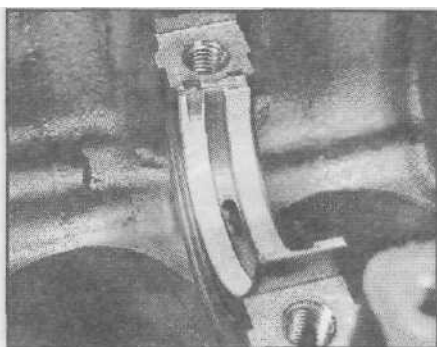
Установка вкладыша центрального коренного подшипника
